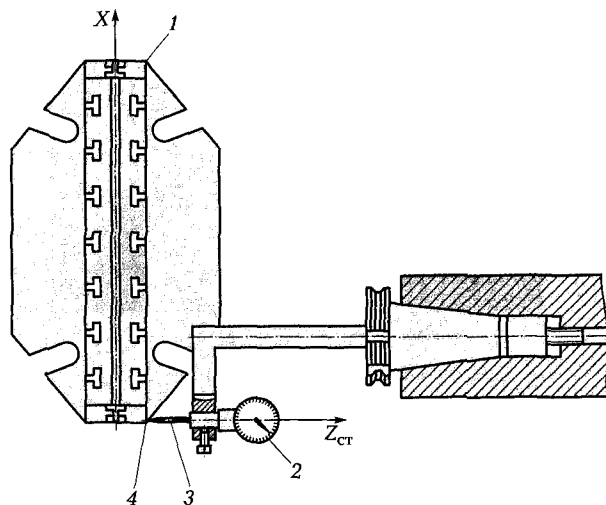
Точки измерения положения приспособления в направлении оси X :
